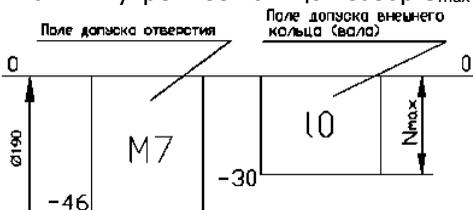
Схема расположения полей допусков соединения «отверстие в корпусе - наружное кольцо».
